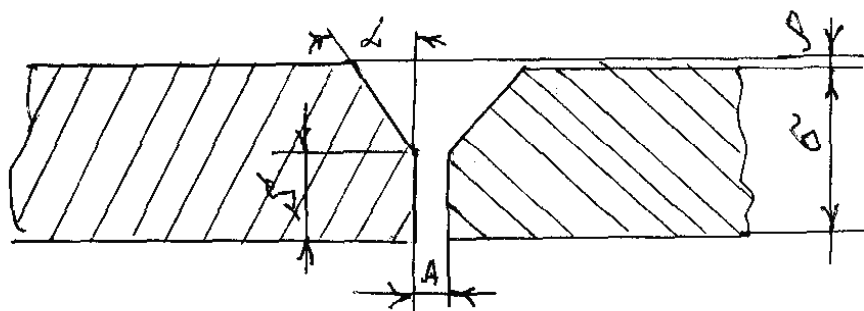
Положение кромок труб перед сваркой встык:
